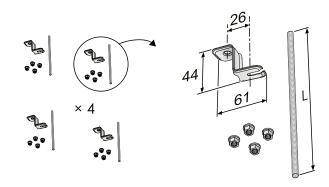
Élément d'assemblage SYST MS M8-1, installation au plafond et sur tige filetée
